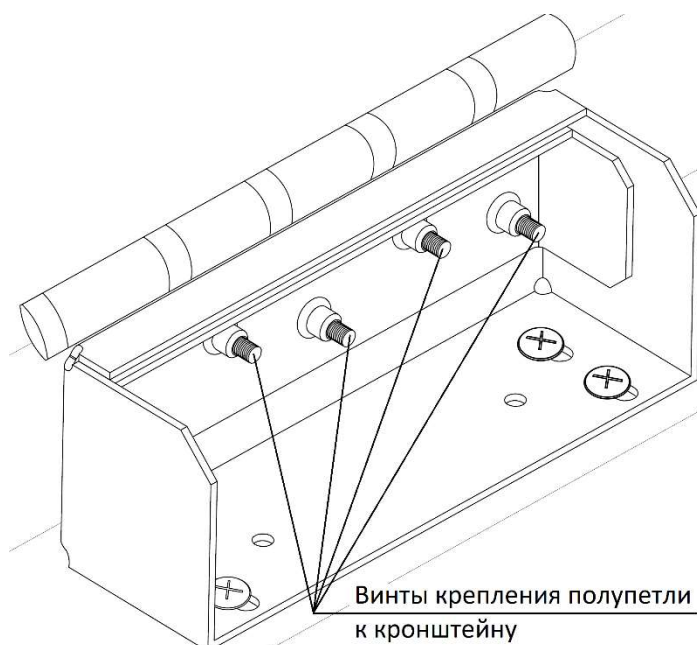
Кронштейн. Регулировка прижима уплотнителя
